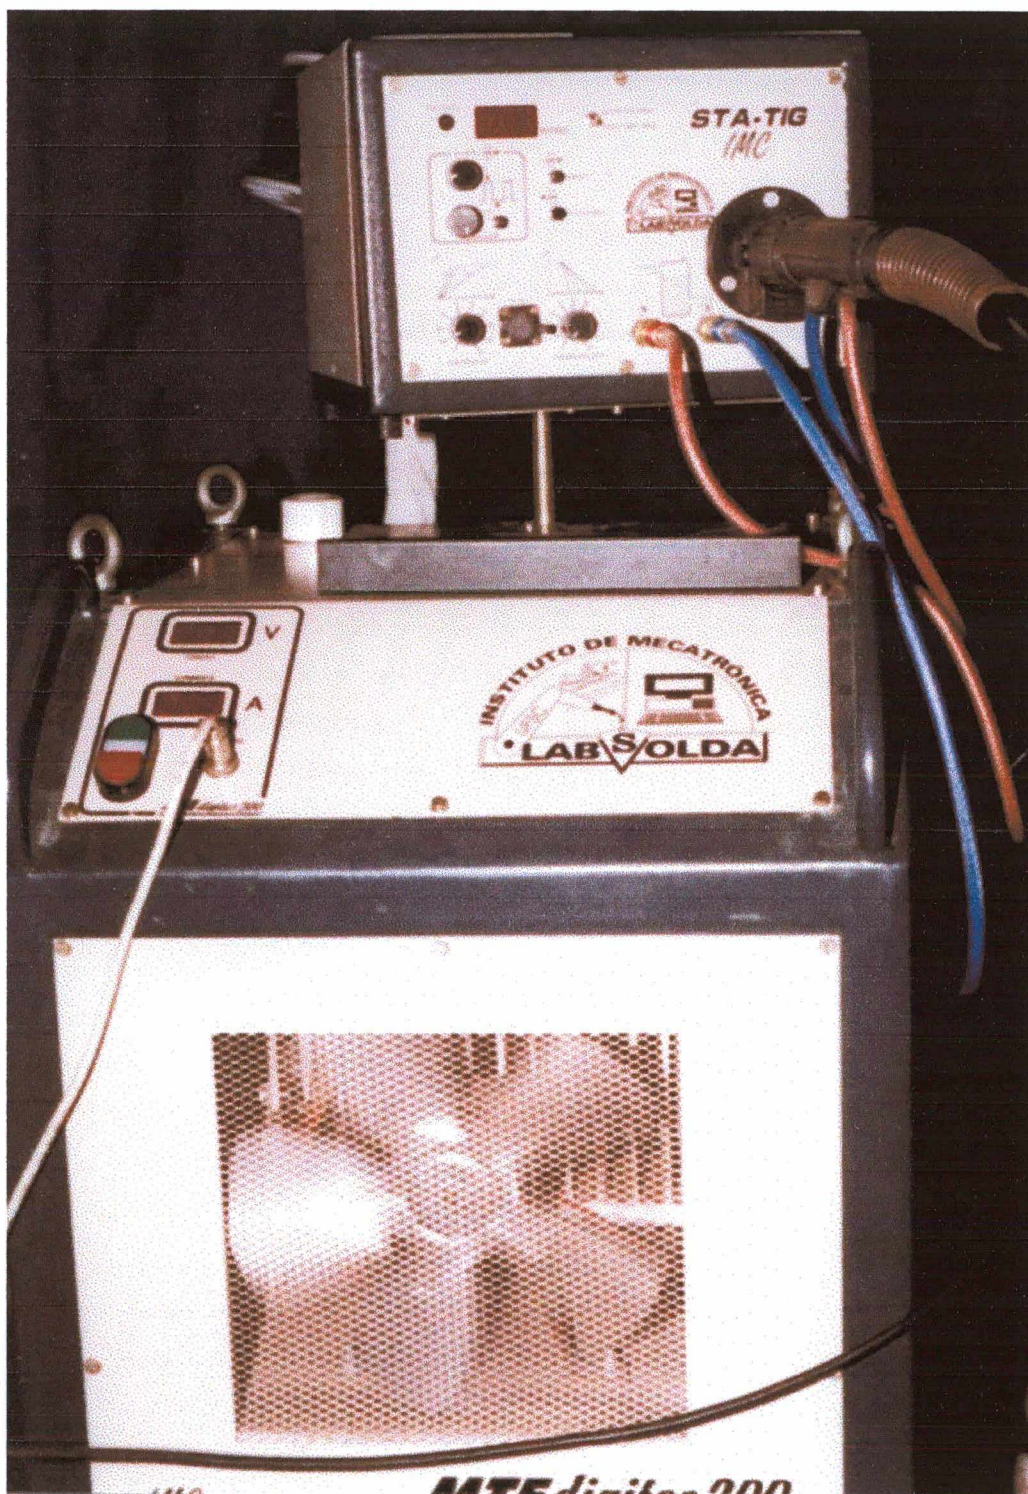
Fonte de Soldagem “MTE DIGITEC 300”, com o cabeçote alimentador de arame “STA – TIG”.
